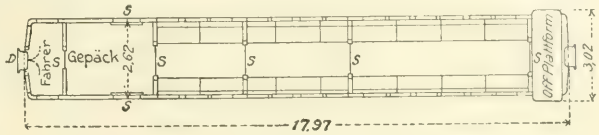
Grundriß eines Wagens der Merseytunnelbahn.
